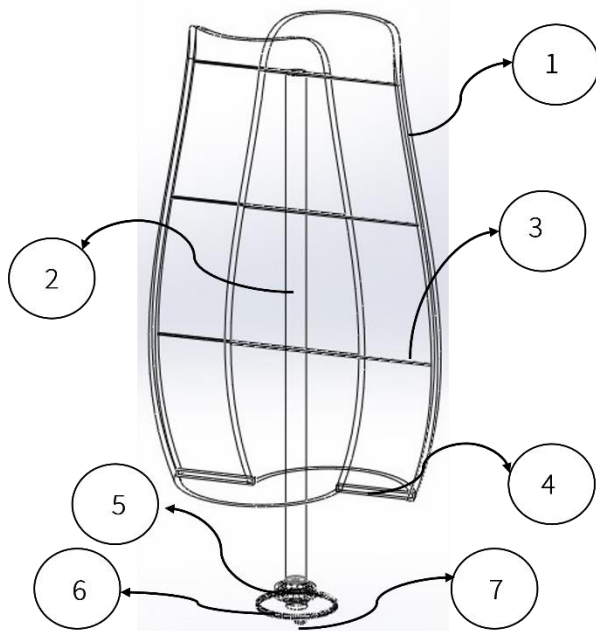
Componentes de la turbina eólica de Tulipán por ser diseñados.
